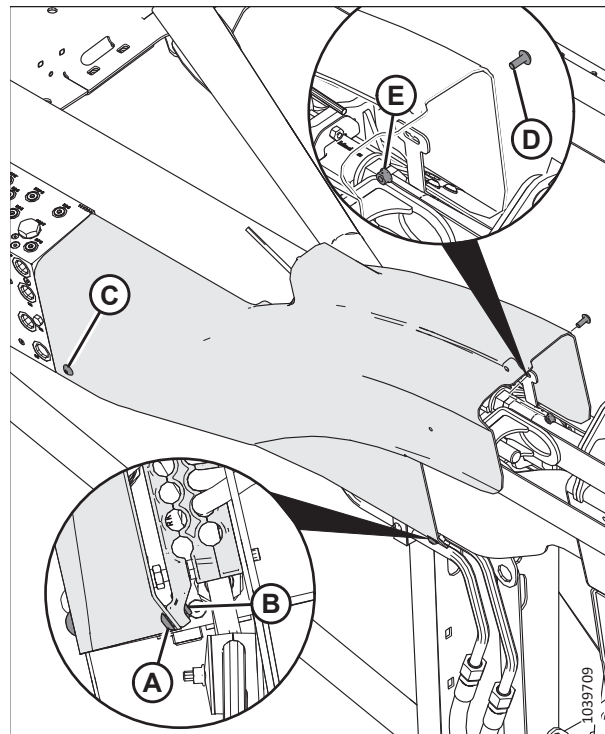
Levý kryt spojovacího ústrojí – zadní část adaptéru
